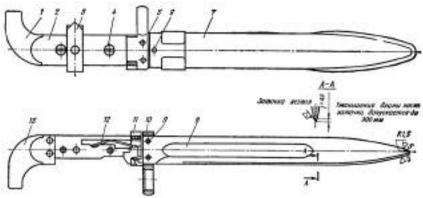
Штык автомата АК (индекс 56-X-212): 1— штык в сборе; 2— щечка правая и щечка левая; 3— ремешок в сборе; 4— винт с гайкой; 5— фиксатор клинка; 6— заклепка обоймы фиксатора; 7— ножна; 5— лезвие в сборе; 5— штифт кольца; 10— кольцо; 11— защелка; 12— пружина защелки; 13— наконечник
